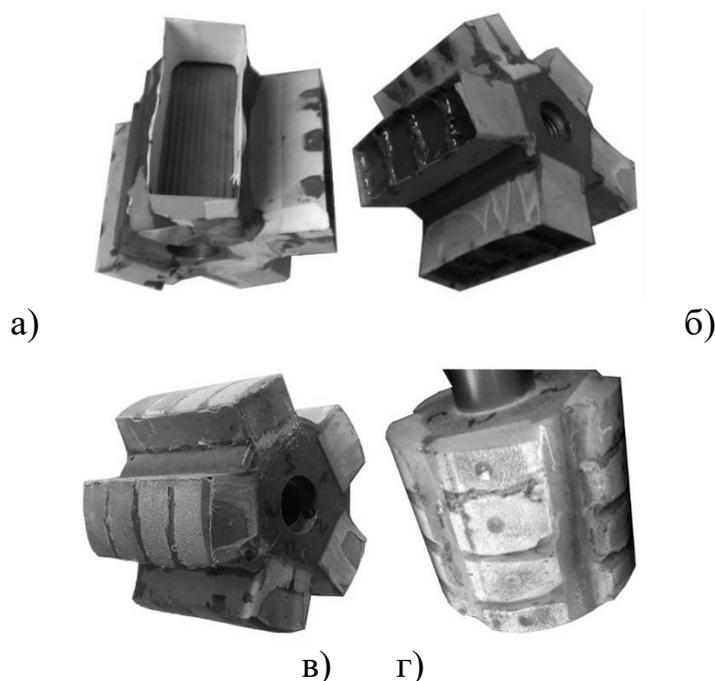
Подготовка образца к испытаниям: а – форма; б – образец с отвержденным композитом; в – образец после механической обработки - точения; г – образец с высверленными лунками
